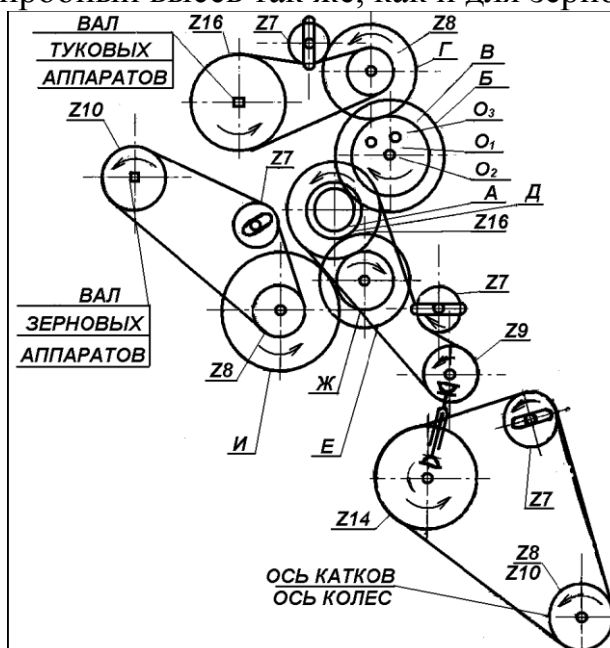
Схема механизма передач в редукторе сеялки СЗП-3,6
